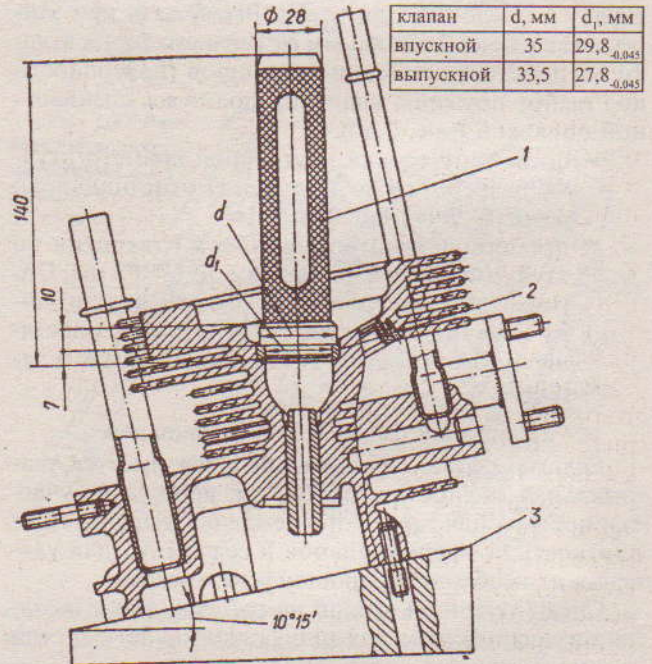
Оправка для запрессовки седла клапана: 1 - оправка; 2 - седло клапана; 3 - подставка
